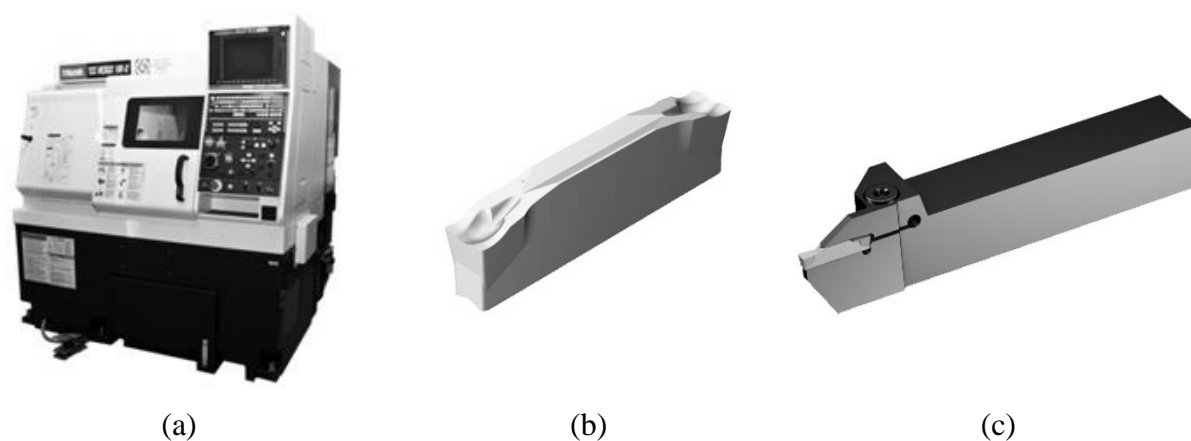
Máquina-ferramenta e ferramenta de corte: (a) torno CNC Mazak QTN 100-II; (b) inserto de metal duro; (c) suporte com inserto fixado.
